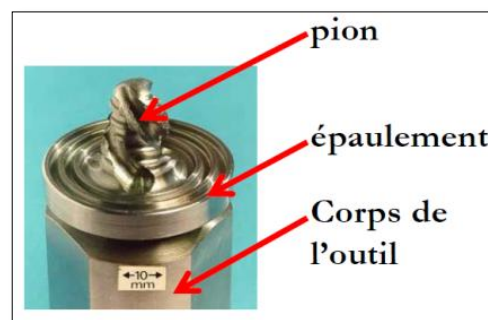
Exemple d'un Outil de soudage FSW [31].
